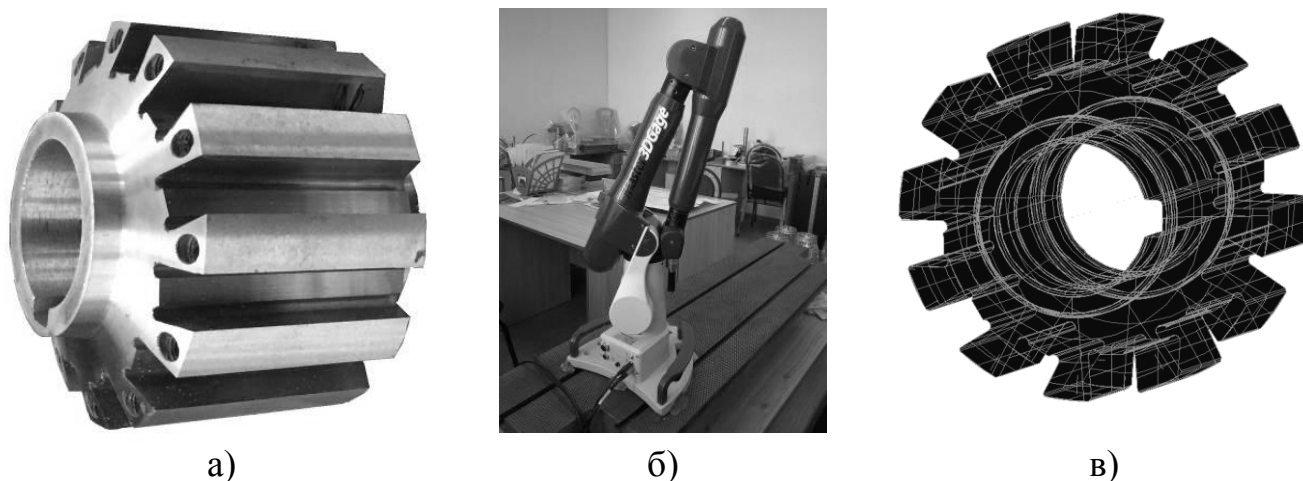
Контроль геометрической точности корпуса фрезы:
